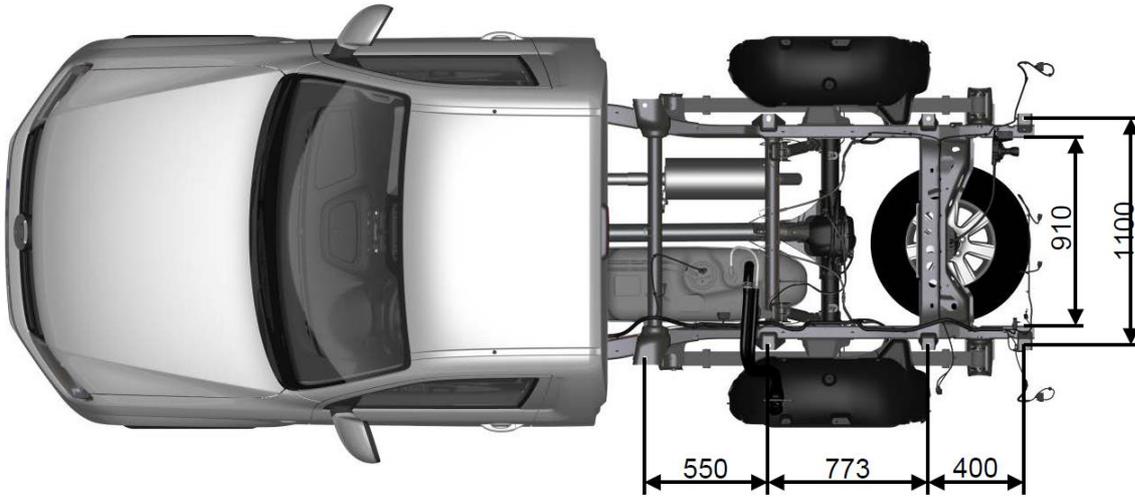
Vista de planta Amarok SC (Single Cab) sin Cargobox
